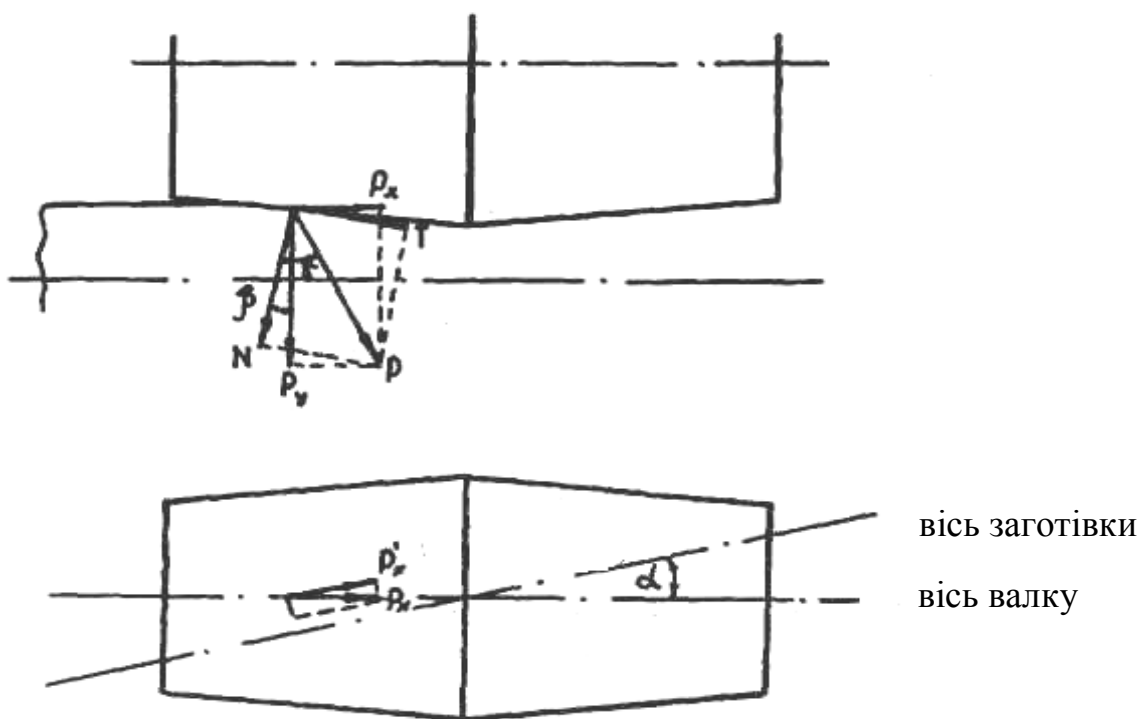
Схема сил, що діють в осередку деформації в момент захоплення заготовки валками
